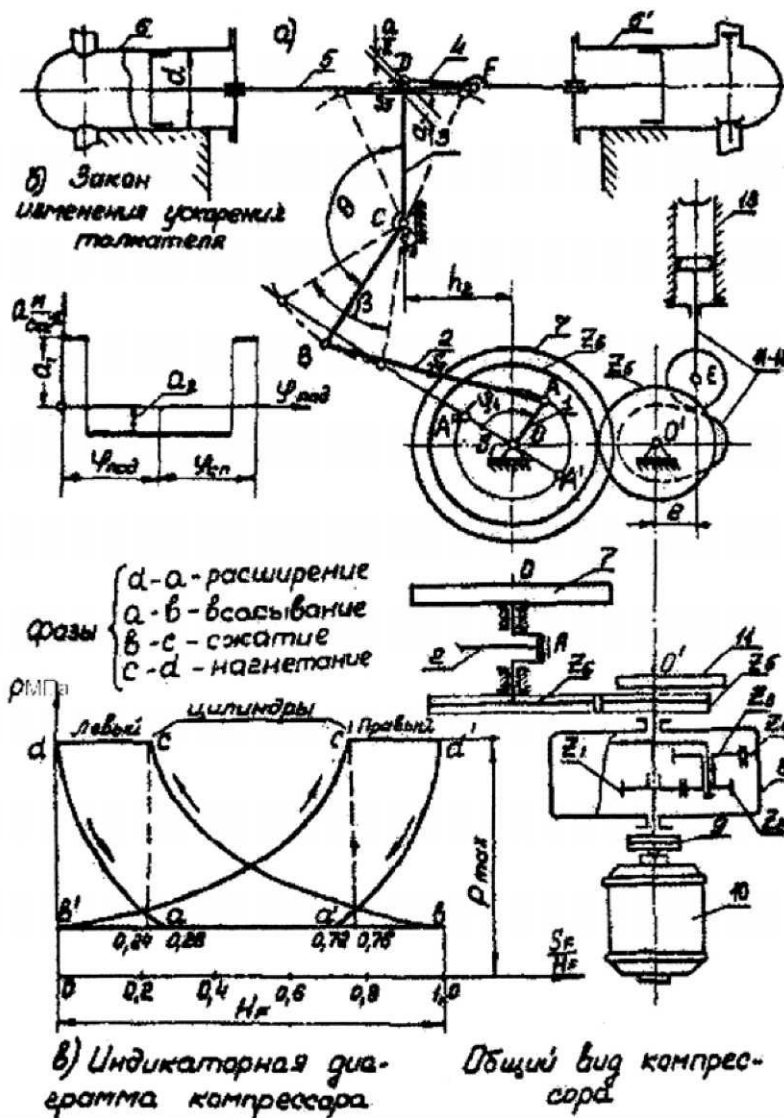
Кислородный двухцилиндровый компрессор: схемы и диаграммы
